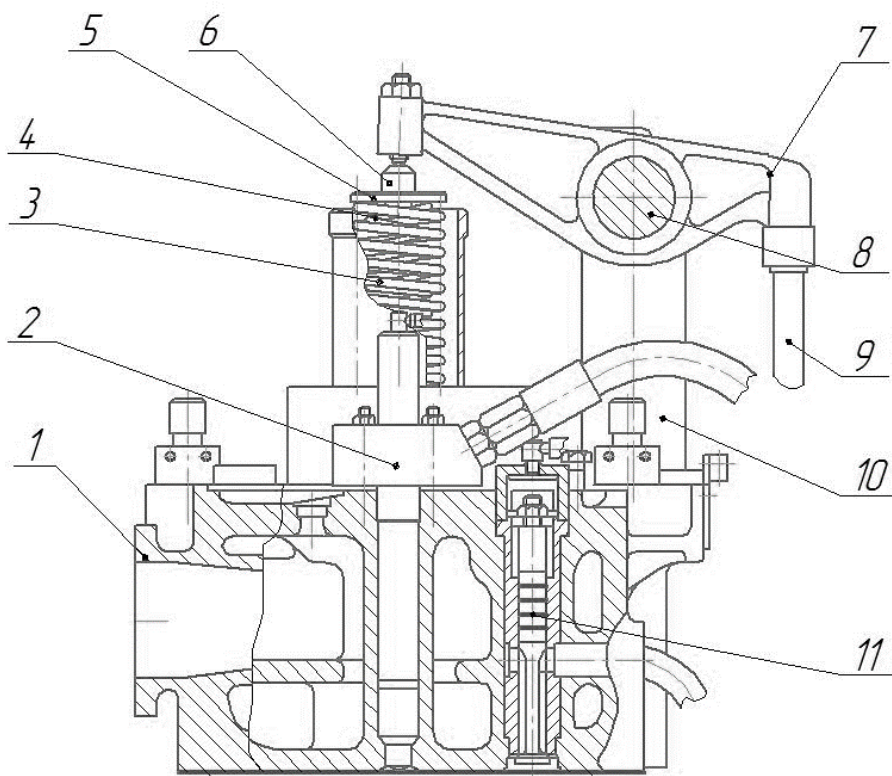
Кришка блоку циліндрів: 1 – корпус головки; 2 – форсунка; 3 – зовнішня пружина клапана; 4 – внутрішня пружина клапану; 5 – верхня тарілка клапану; 6 – клапан; 7 - коромисло; 8 – вісь коромисел; 9 – штанга; 10 – опорна стійка; 11 – повітряний клапан
